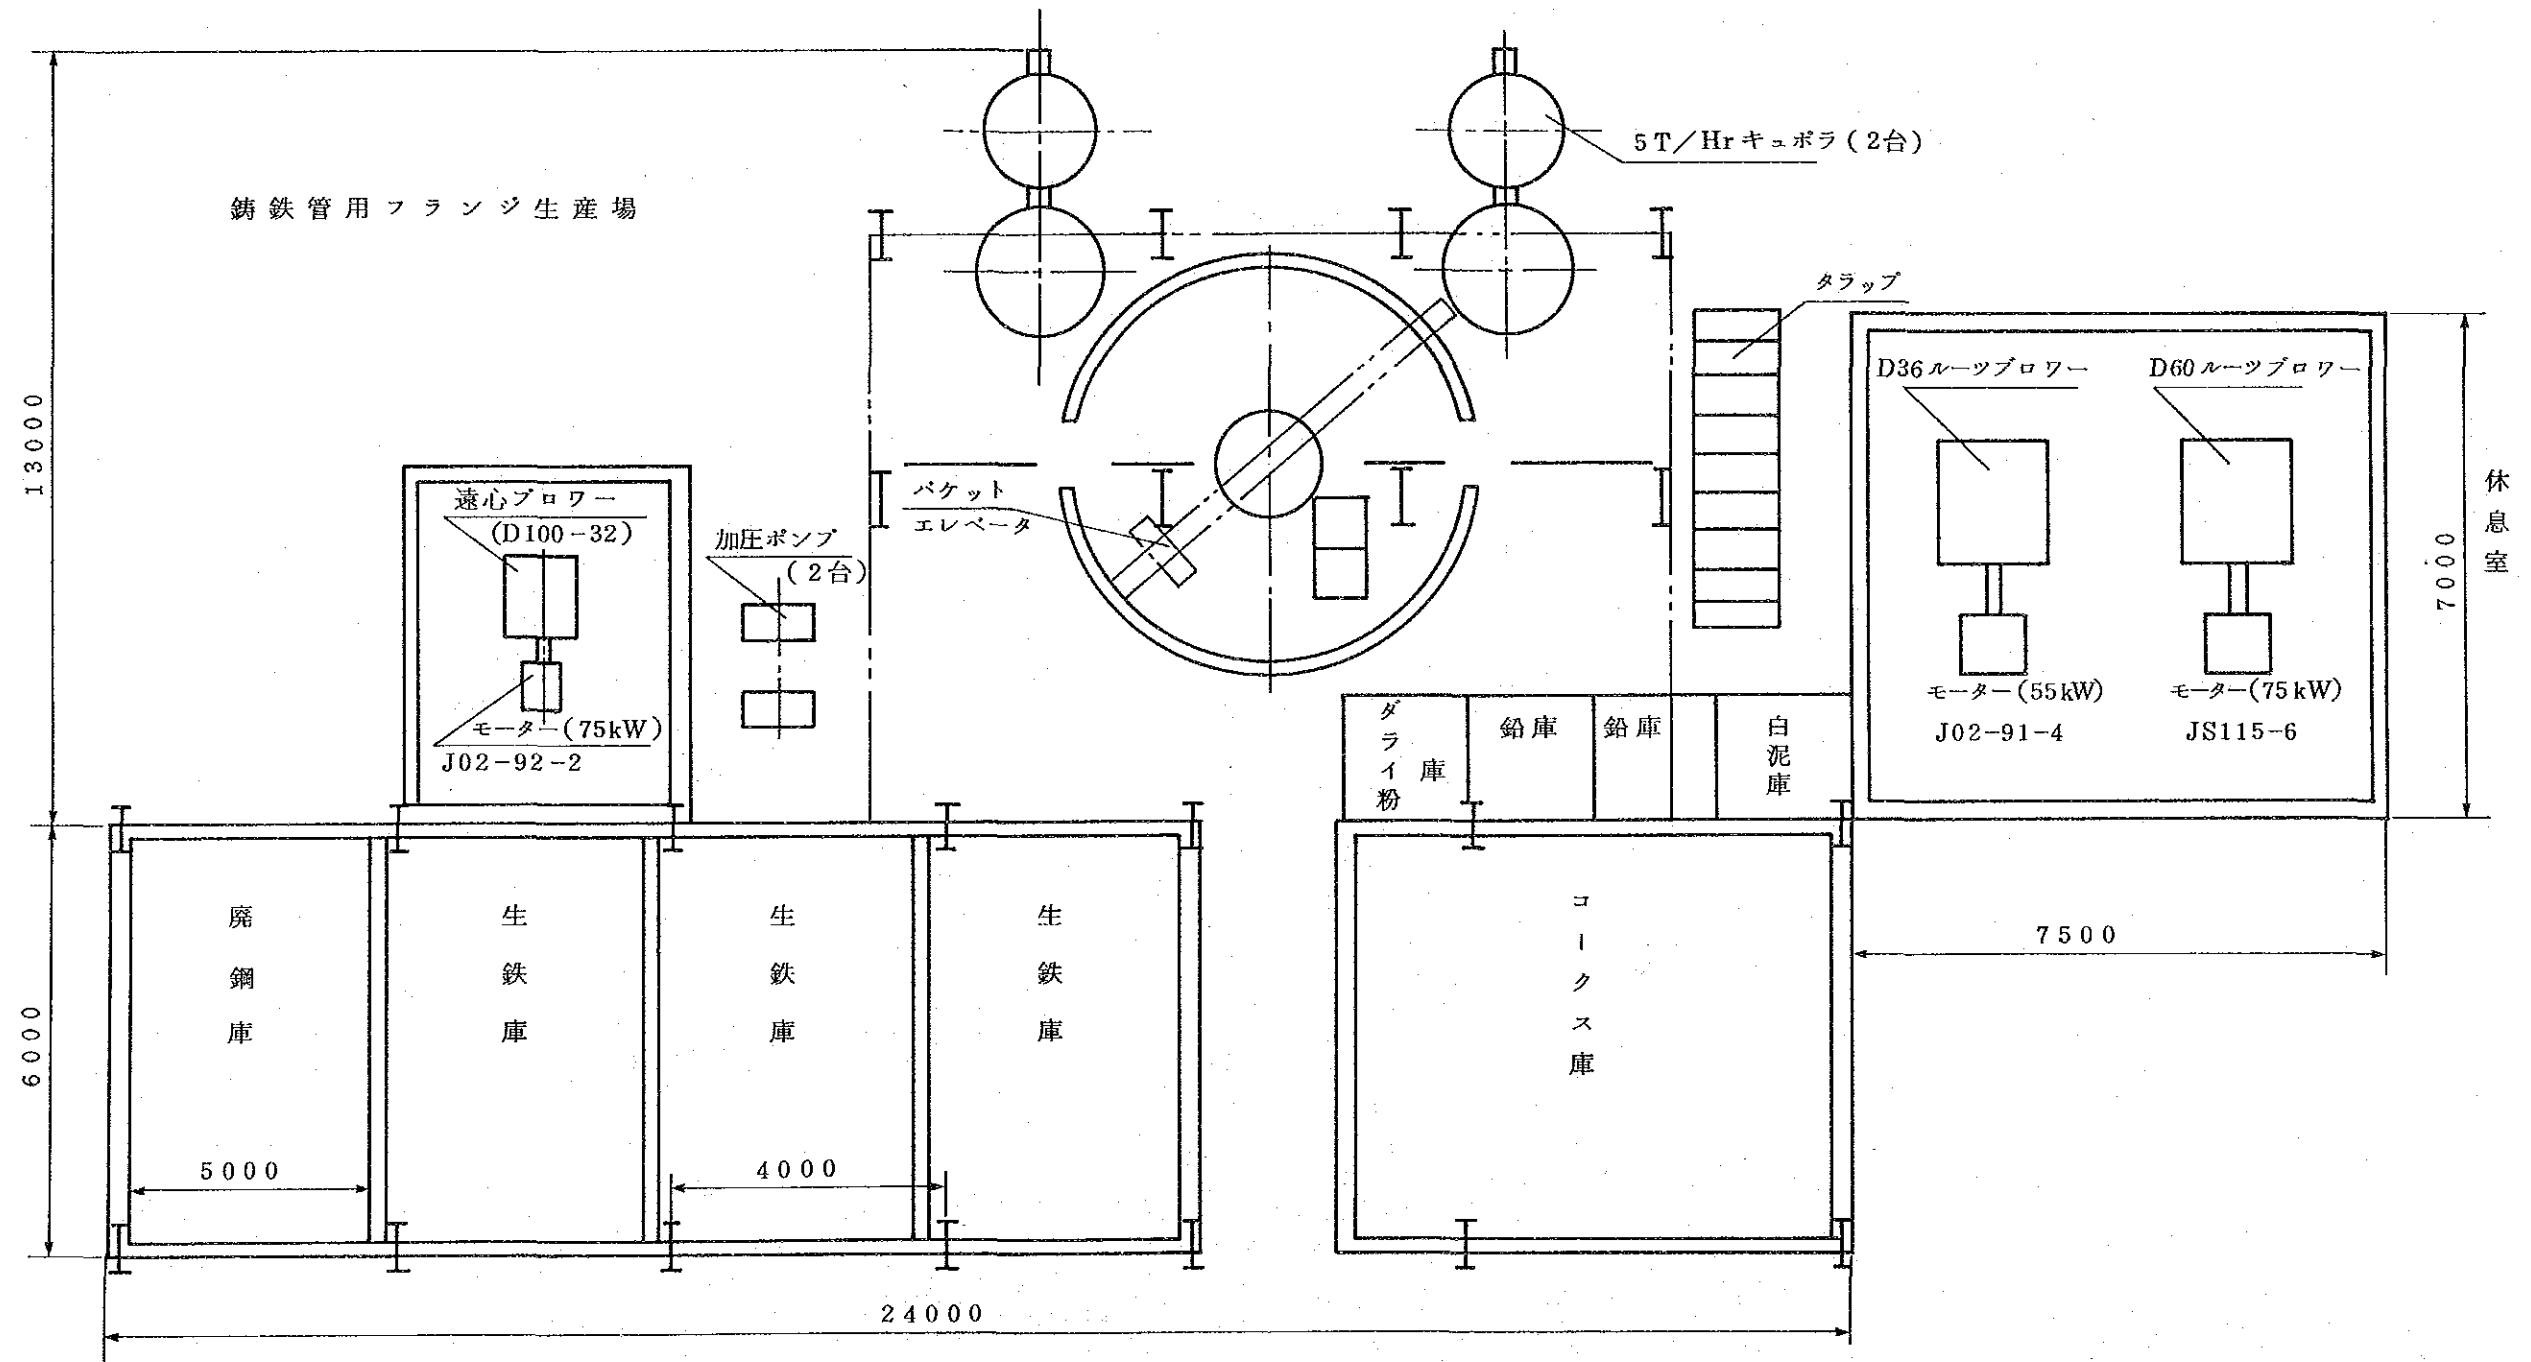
鋳造第二分廠手込造型ラインの溶解場平面配置図
